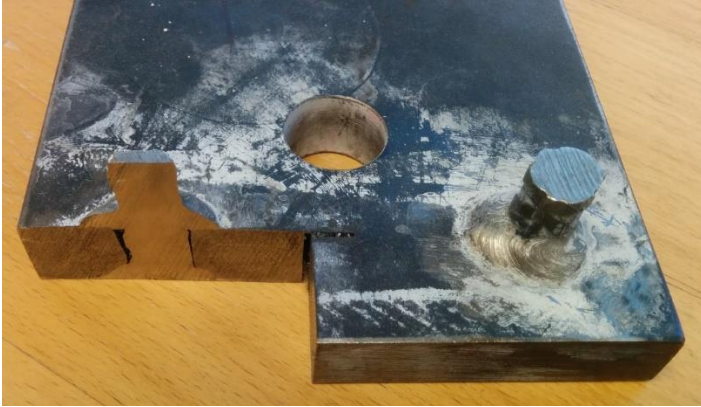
Nicht geglückte Probeschweißung zur Entwicklung der Schweißanweisung
